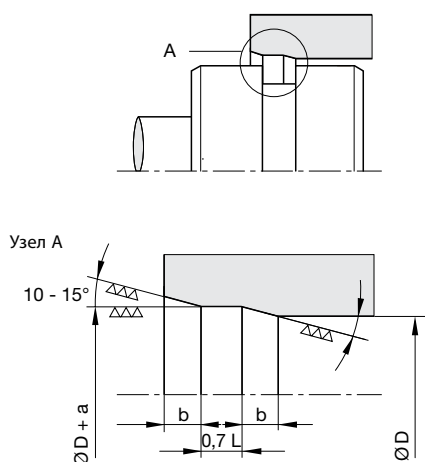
Slipper Seal®поршневого типа, установка, шаг 2. Рекомендуемая заходная фаска для установки уплотнения Slipper Seal® поршневого типа.
